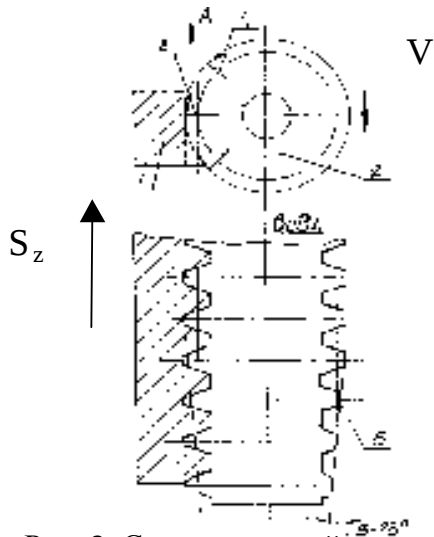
Схема чистової обробки зубів рейки черв'ячною фрезой
